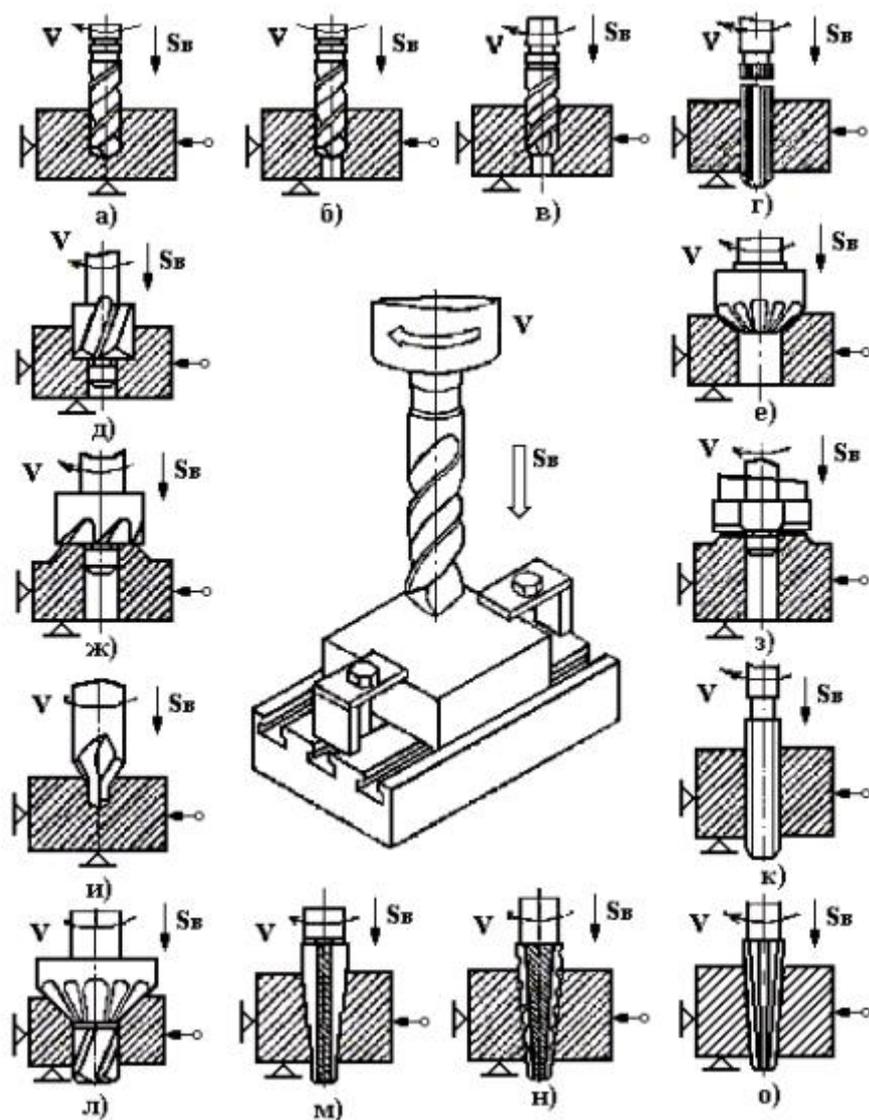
Схемы обработки поверхностей на сверлильных станках: а – сверление; б – рассверливание; в – зенкерование; г – развертывание; д – цилиндрический зенкер (зенковка); е – конический зенкер (зенковка); ж – цековка; з – пластинчатый резец; и – центровочное сверло; к – метчик; л – комбинированный инструмент; м – конический зенкер; н, о – конические развертки.
